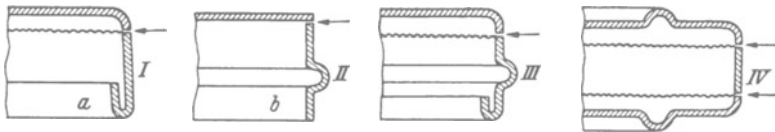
Beispiele von Schweißarbeiten an Radschutzkästen.
